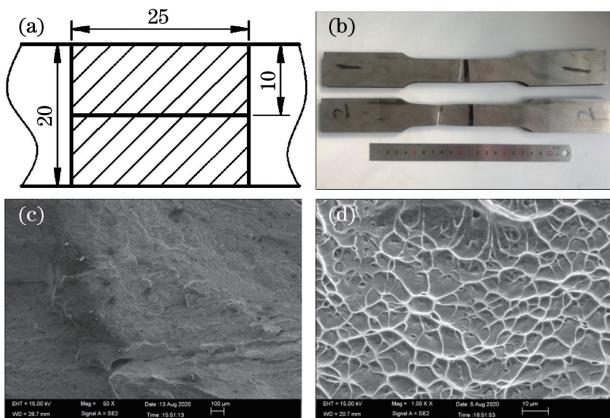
拉伸试样取样位置、断裂位置及断口形貌。(a)取样位置;(b)断裂位置;(c)断口形貌 50 倍;(d)断口形貌 1000 倍
